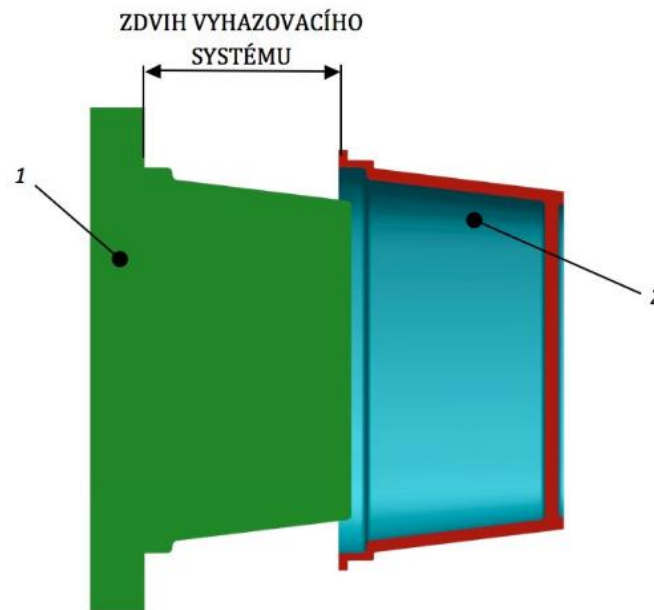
Příklad obecného rozložení vybraných komponent (převzato z [6])
